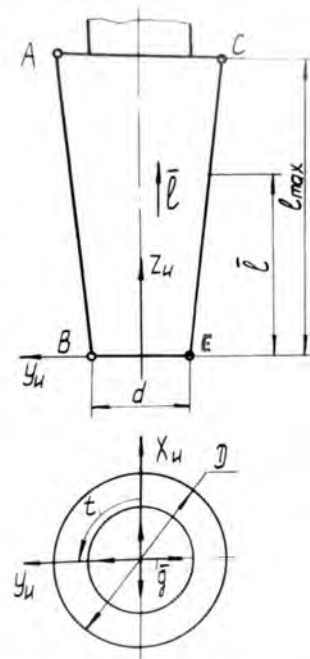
Параметри кінцевої фрези з конічною ріжучою частиною
